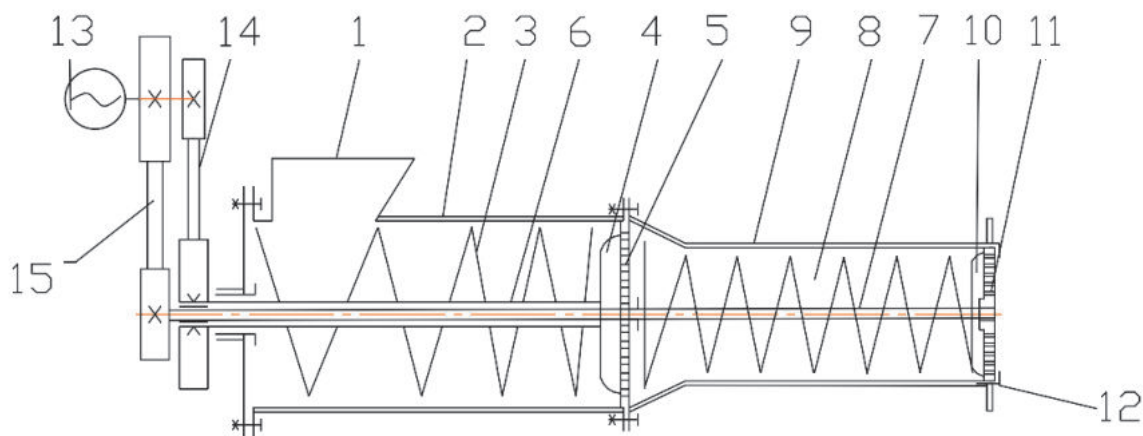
Измельчитель сырья рыбного и нерыбного происхождения: 1 – приемный бункер; 2 – корпус; 3 – подающий шнек, оснащенный режущим узлом; 4 – серповидный нож; 5 – нож-решетка; 6 – полый вал; 7 – вал с нагнетающим шнеком; 8 – нагнетающий шнек; 9 – корпус, оснащенный узлом измельчения; 10 – крестовидный нож; 11 – нож-решетка; 12 – болты для разъема корпусов; 13 – приводной узел, включающий электродвигатель и две приводные передачи; 14, 15 – приводные передачи понижающего и повышающего типа
